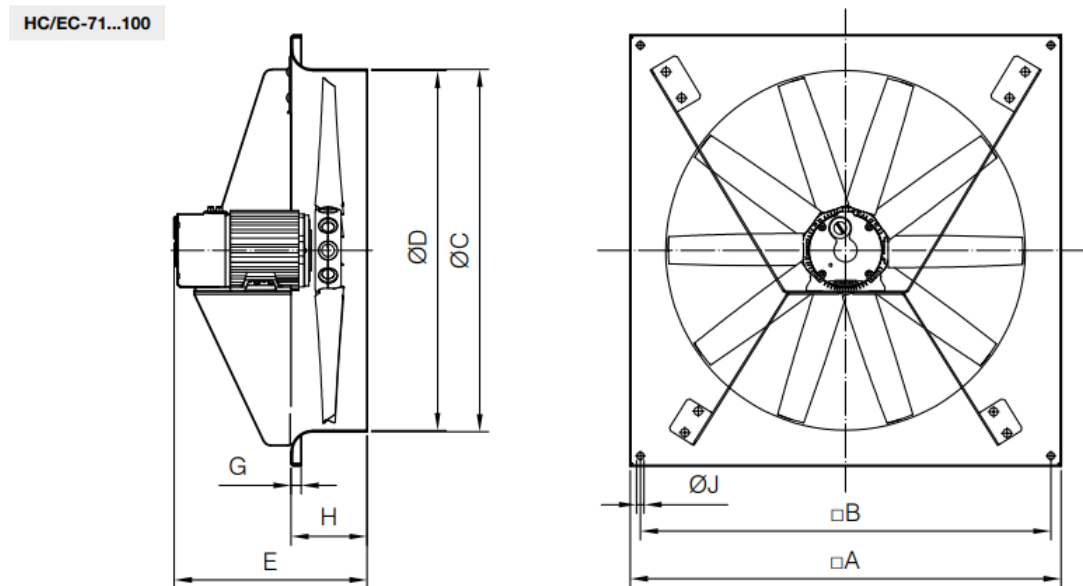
Dimensiones del ventilador seleccionado ventilador. Tomado de [31]
